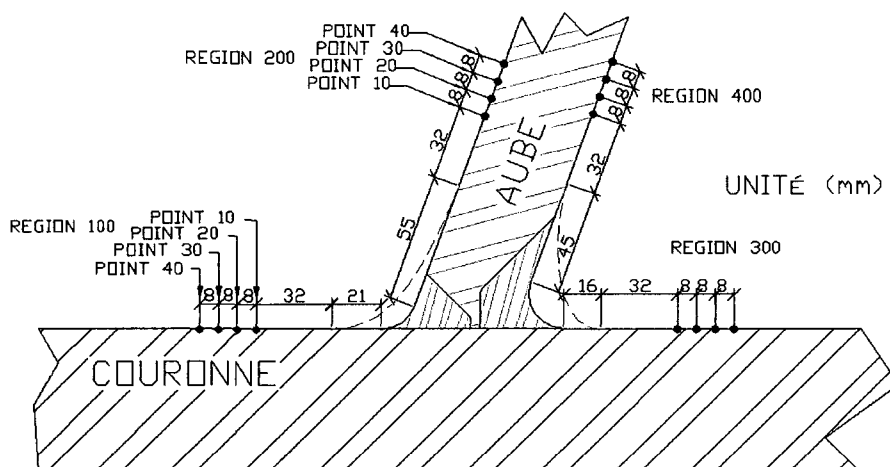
Points de mesure durant le soudage au bord d'attaque
